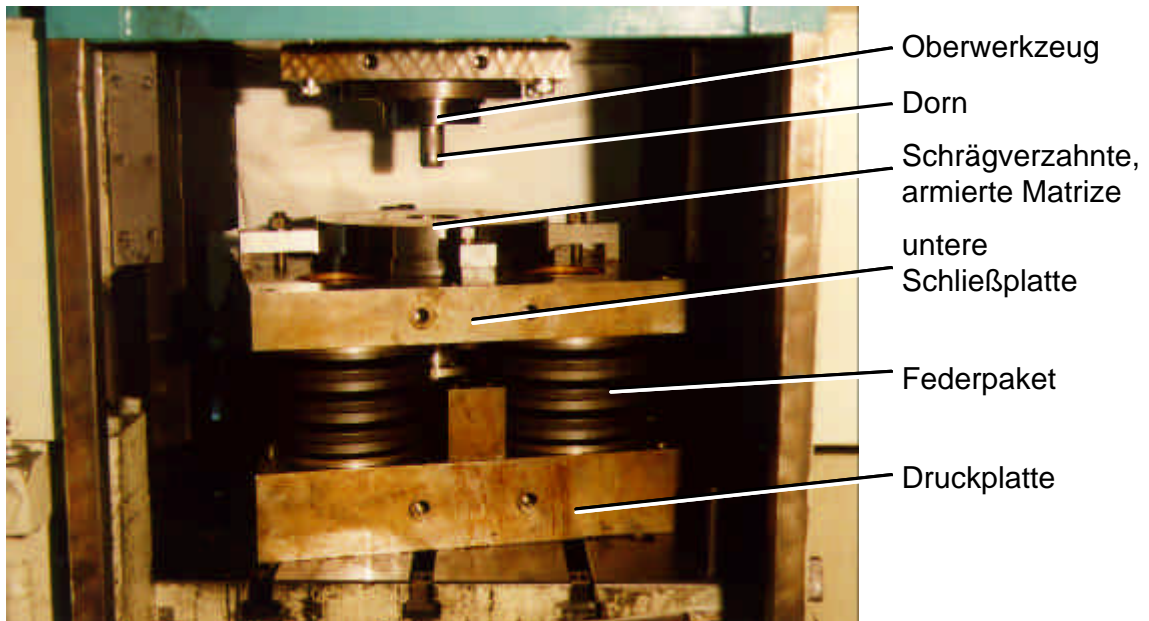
In Presse eingebautes Werkzeugsystem zum Gangrad Schmieden (erste Stufe)
